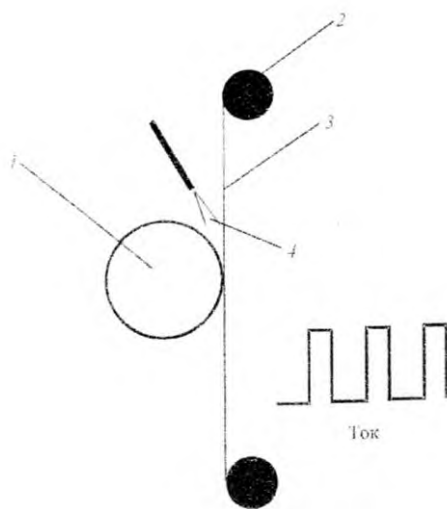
Принцип работы электроэрозионного станка: 1- разрезаемый образец; 2- твердосплавные направляющие; 3- режущая нить; 4- охлаждающая жидкость
